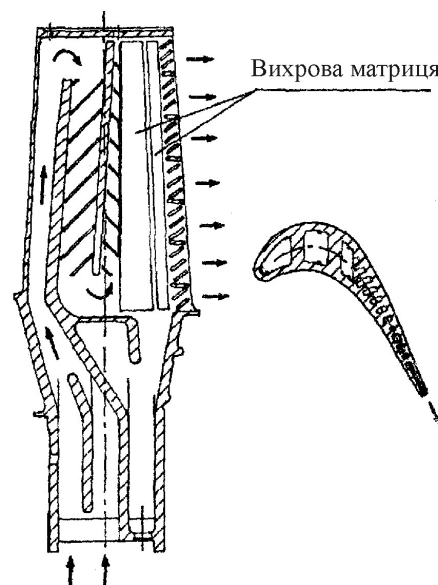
Конструкція охолоджуваної робочої лопатки з вихровою матрицею
